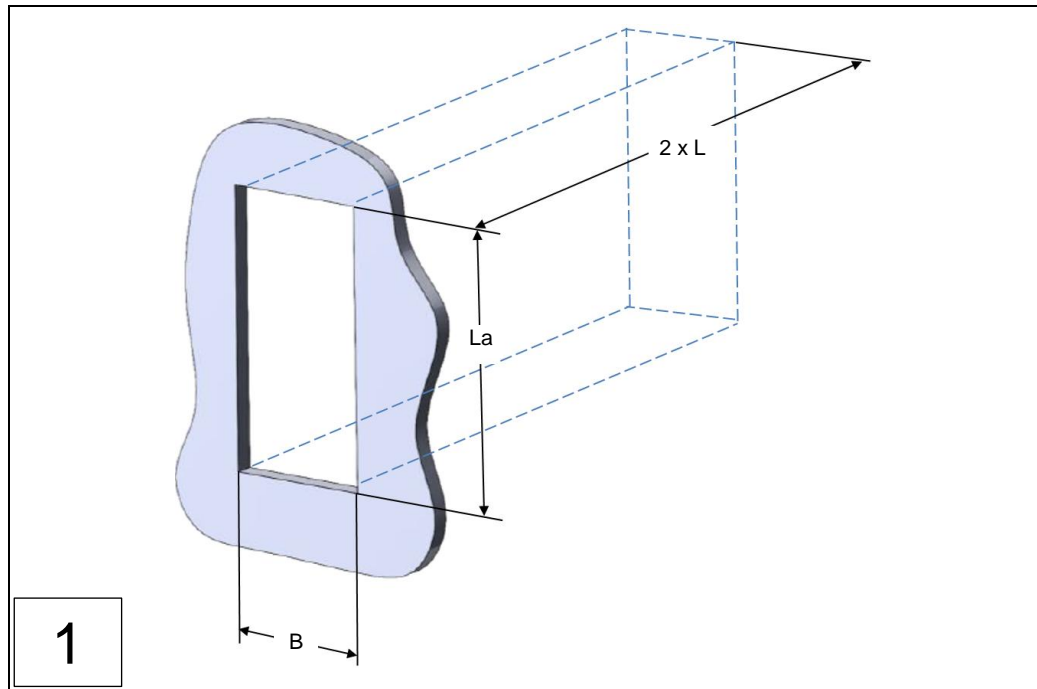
Dimensiones del espacio de instalación, Remote Indicator
